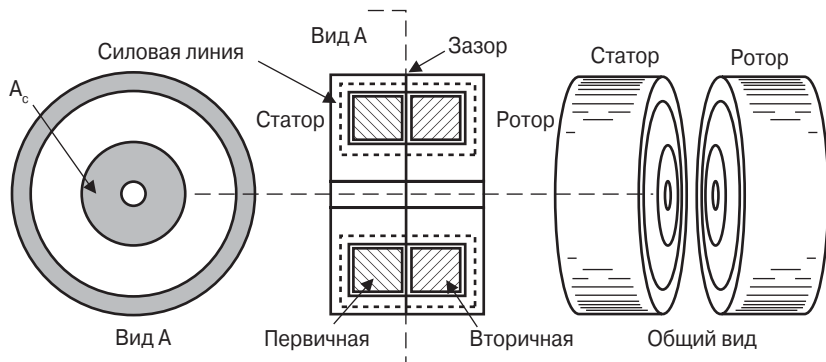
Геометрия базовых типов роторного трансформатора
